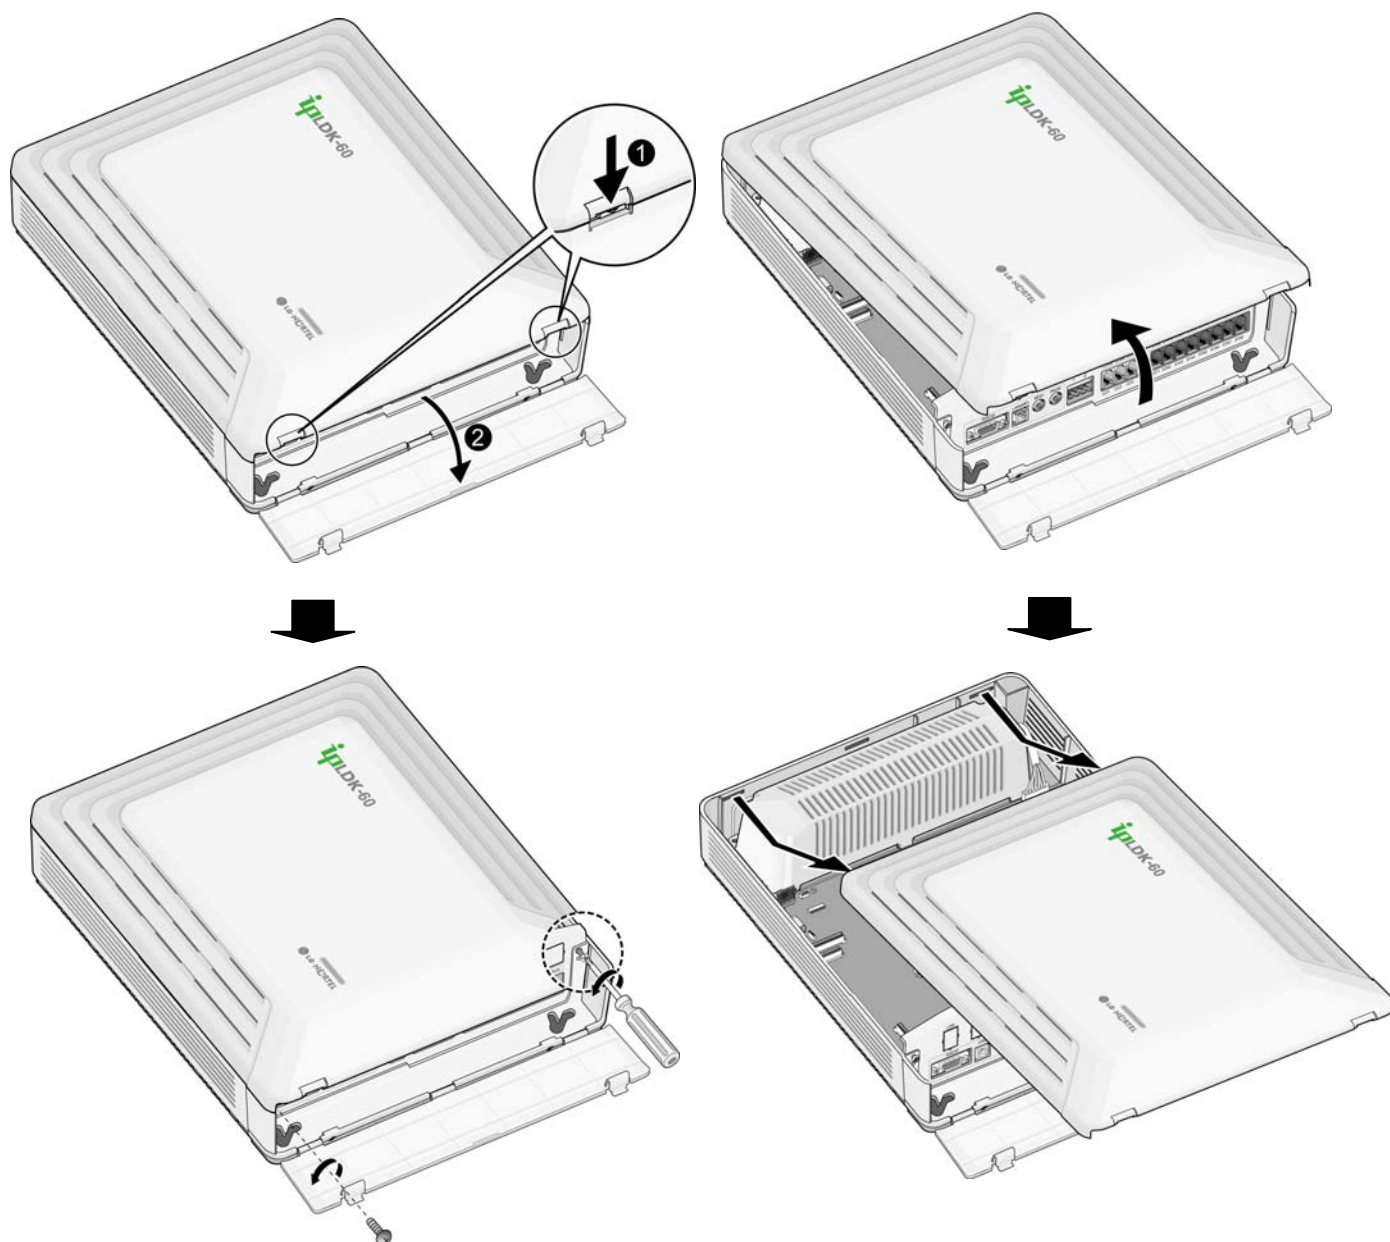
ABRINDO A TAMPA FRONTAL
